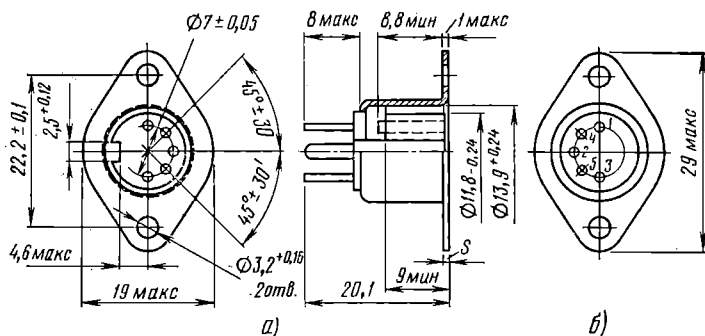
Трех- и пятиконтактные розетки СГЗ и СГ5. В трехконтактной розетке в отверстия не закладываются. (Размер S : 1,5—0,3 — для металла; 3,4—0,3 — для пластмассы)
